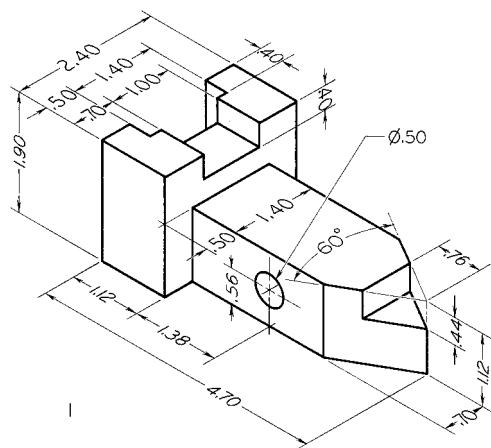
■ Llave de seguridad. (Esquema A-3).
